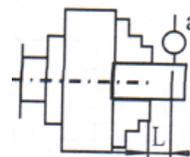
Токарный патрон с креплением за внешнюю поверхность заготовки с помощью прямых кулачков:
